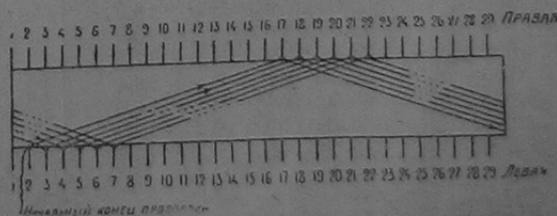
Чертеж болванки в развернутом виде, показывающий способ намотки
